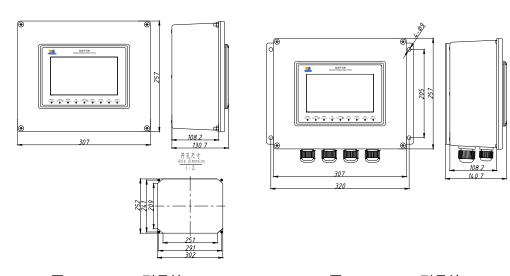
KZM-1ZQ 型母钟 Fig.12 KZM-1ZQ master clock
